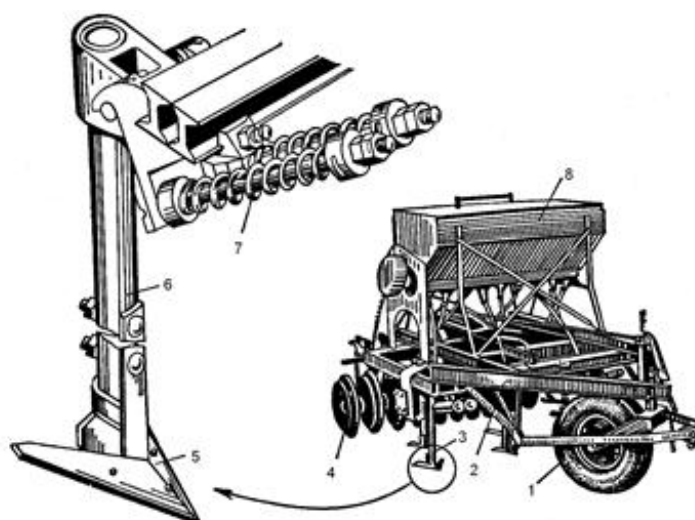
Зерновая стерневая сеялка и ее рабочий орган: 1- колесо; 2-рама; 3-сошник; 4-катки; 5-лапа; 6-стойка.
